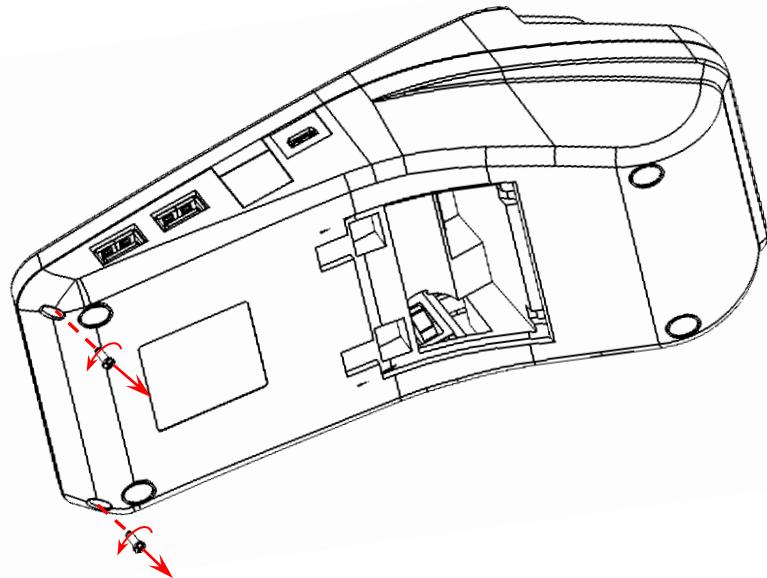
Винты крепления нижней части корпуса к верхней части
